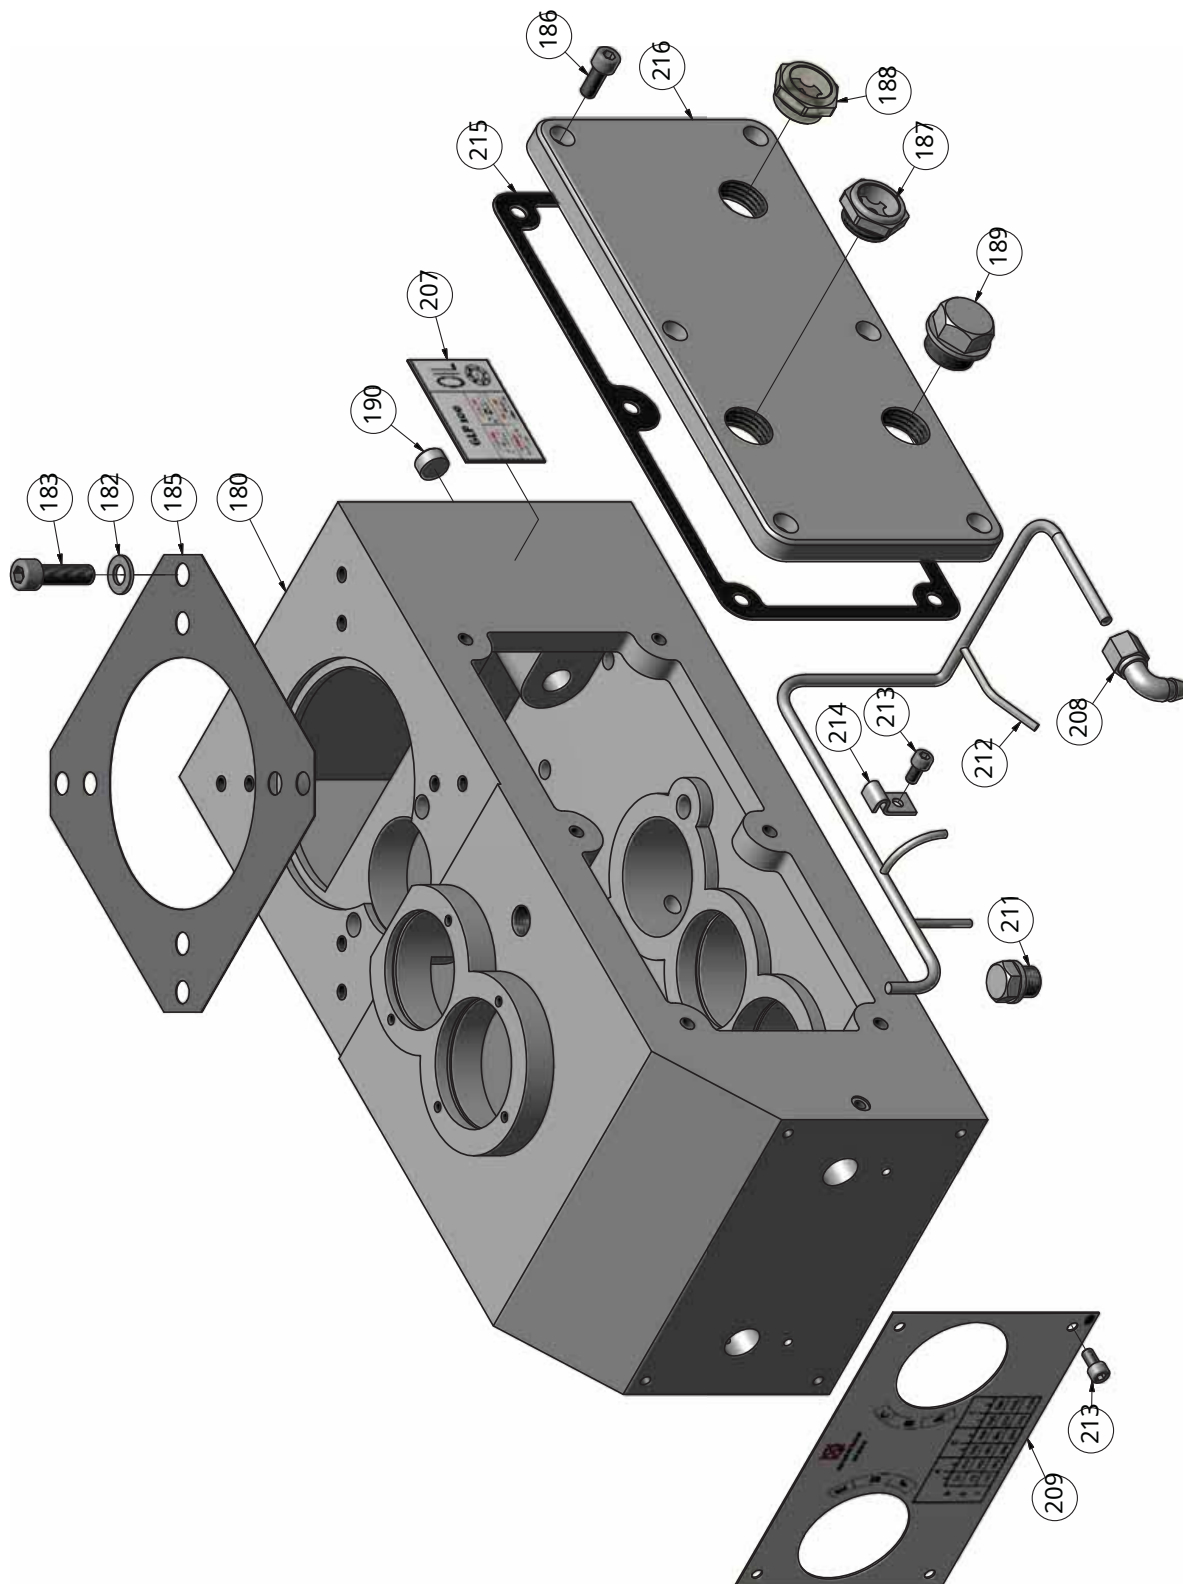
Getriebe Bohrspindel 4 de 4 - Husillo principal de caja de cambios 4 de 4
